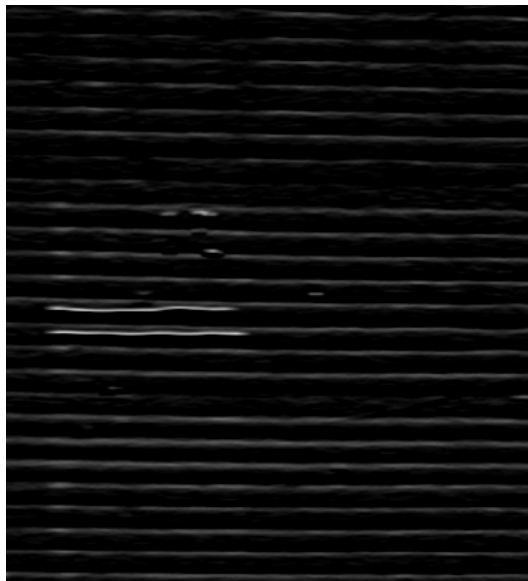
Imagen de prueba sin separación entre carriles
